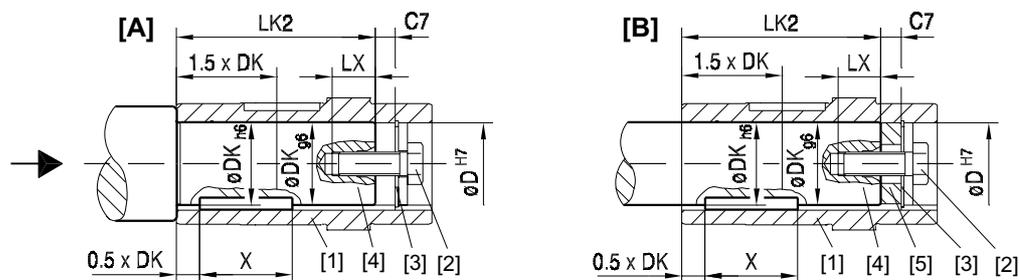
Ведомый вал с опорным выступом (A) и без опорного выступа (B)
